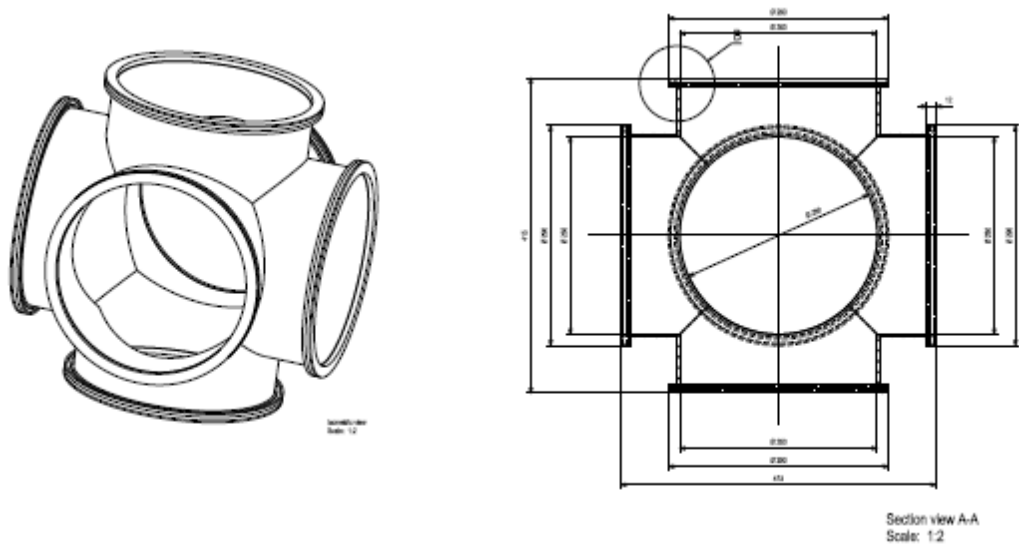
Vista 3D e sezione della camera da vuoto.
